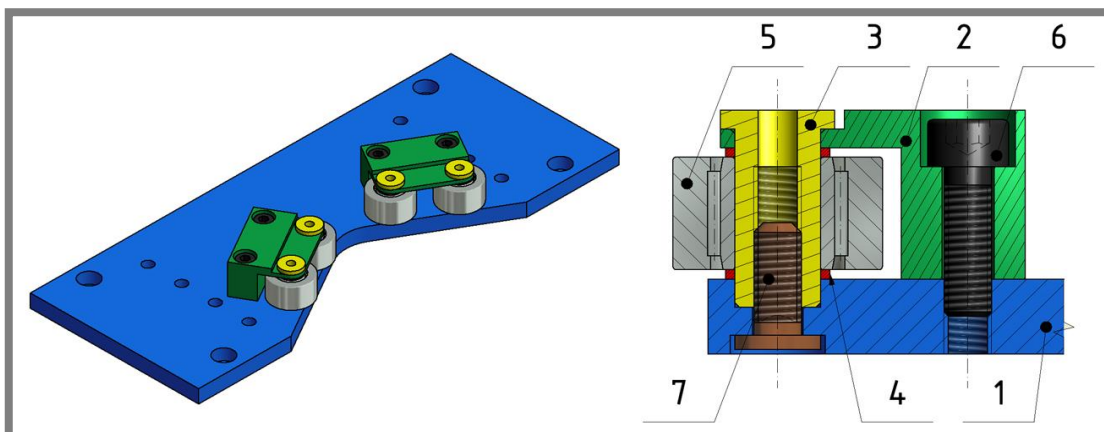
Varianta 3 – Deska se zapuštěnou točnou
